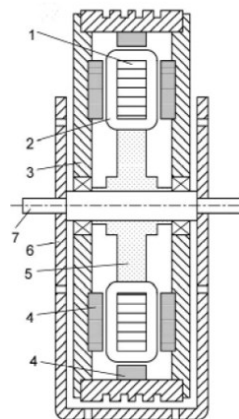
Machine hybride à flux radial et axial : 1 - stator, 2 – enroulements stator, 3 - rotor, 4 – aimant permanent, 5 - résine, 6 - châssis, 7 - arbre [10]
